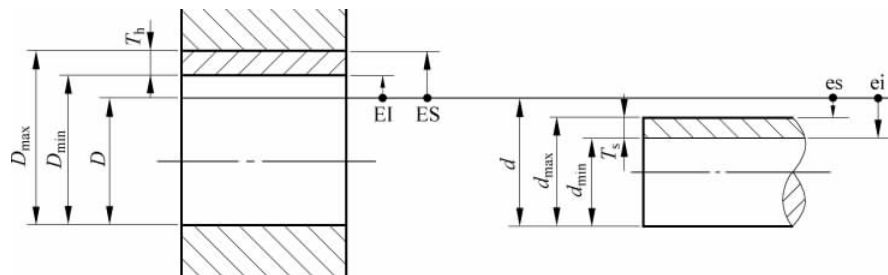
公称尺寸、上极限尺寸、下极限尺寸、上极限偏差、下极限偏差、尺寸公差
